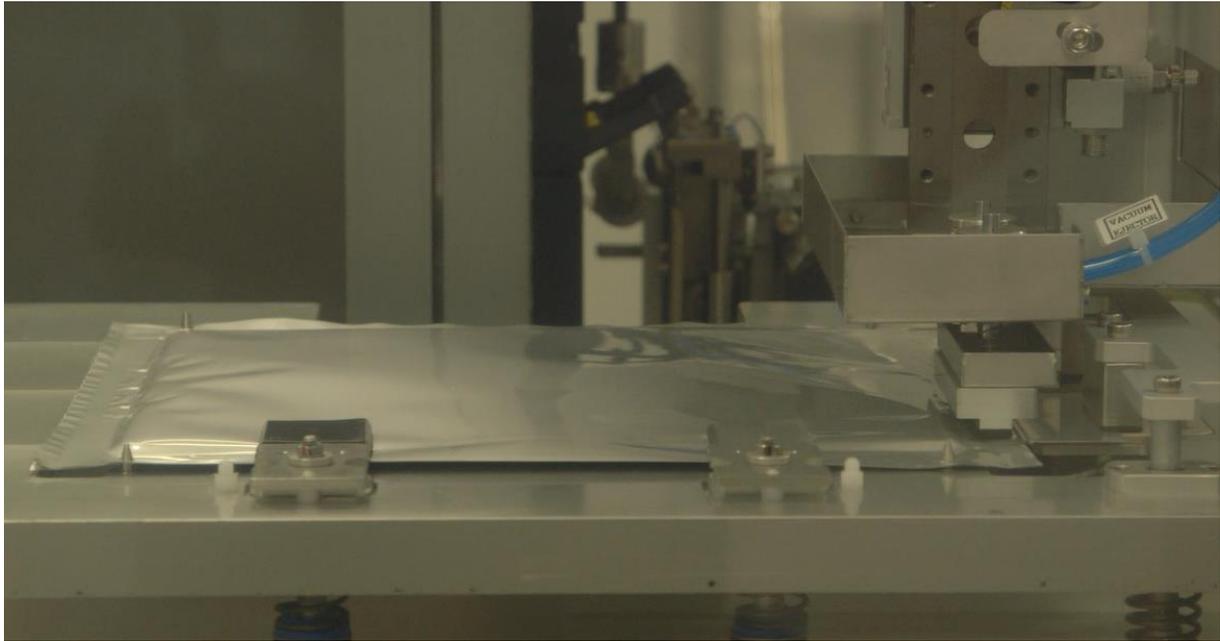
Thermo soudure des feuillets aluminium (3 côtés)
